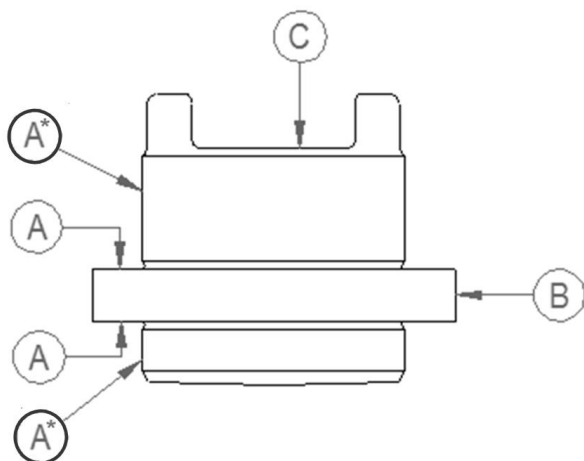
Ведущая втулка с кулачками от НОВЗ, важные поверхности
